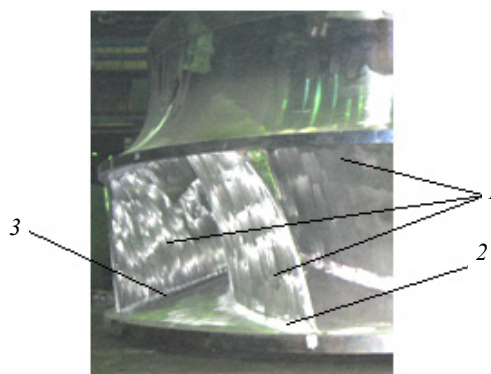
Фрагмент рабочего колеса турбины: 1 – плоскости лопаток; 2 – правый нижний сварочный шов; 3 – левый нижний сварочный шов
